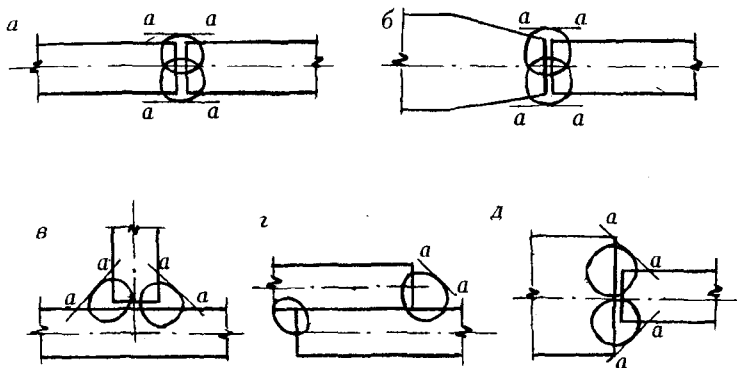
Сварные соединения: а, б — соединения со стыковыми швами; в, г, д — с угловым
